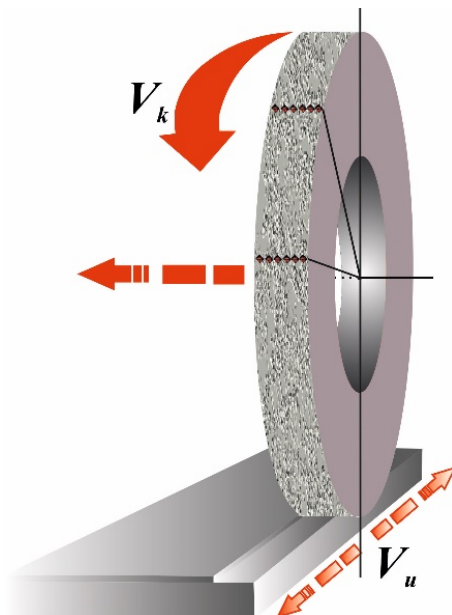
Схема образования шлифованной поверхности при моделировании рабочей поверхности круга элементарными режущими профилями
